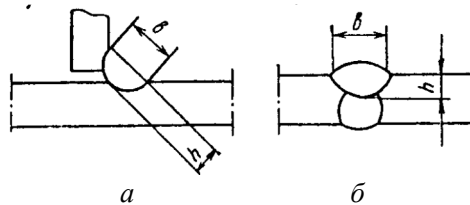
Форма провару зварних з'єднань: а – кутового шва; б – стикового однопрохідного шва
